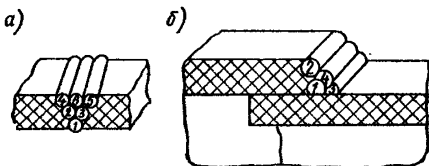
Порядок укладки сварочных прутков в шов
